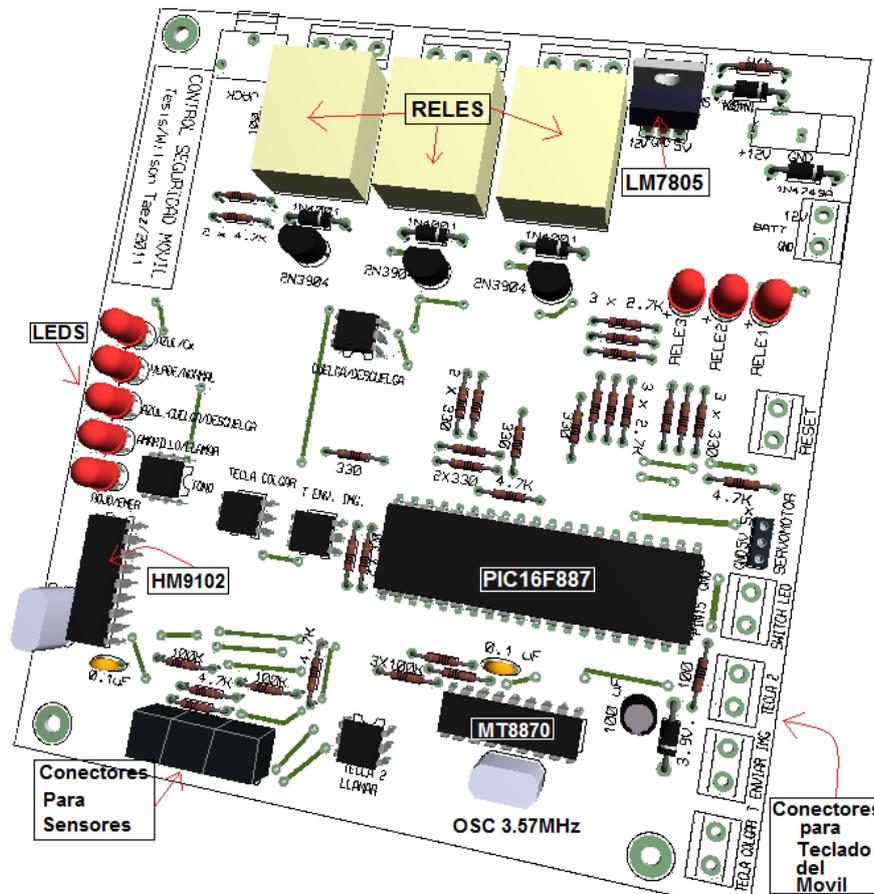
Vista en 3D de la ubicación de elementos en la placa principal (Fuente: propia)
